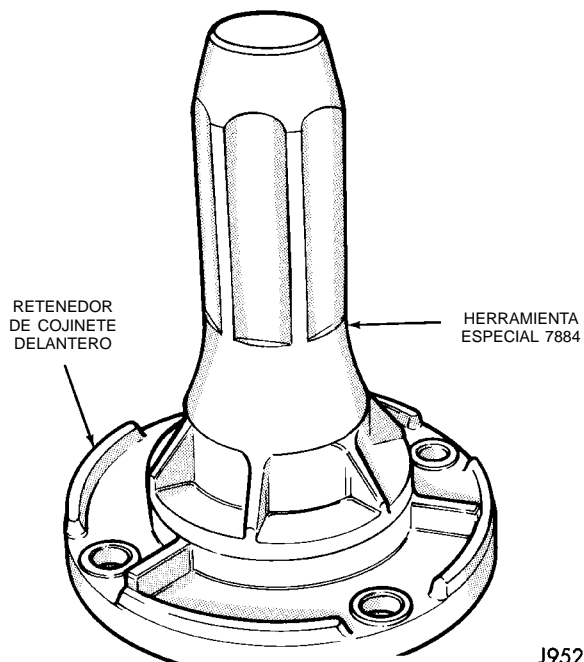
Instalación del cojinete de guía del engranaje impulsor
